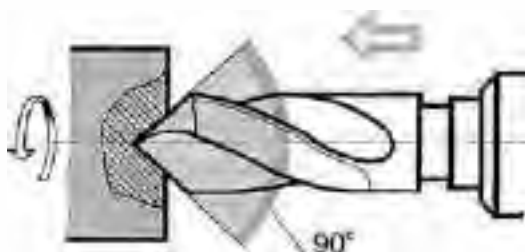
ЗАСВЕРДЛЮВАННЯ ТОРЦЯ ЗАГОТОВКИ
